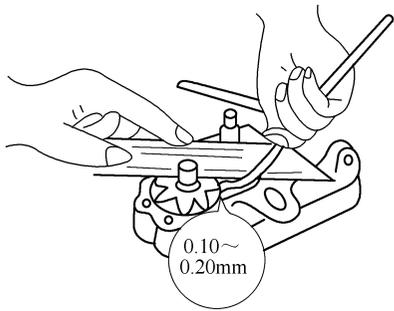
齿轮式机油泵齿轮端面与泵盖间隙
